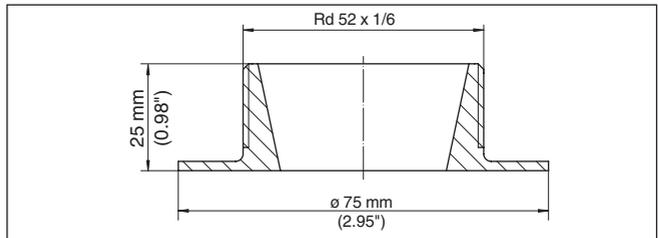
Dimensions raccord à souder raccord conique DN 25
